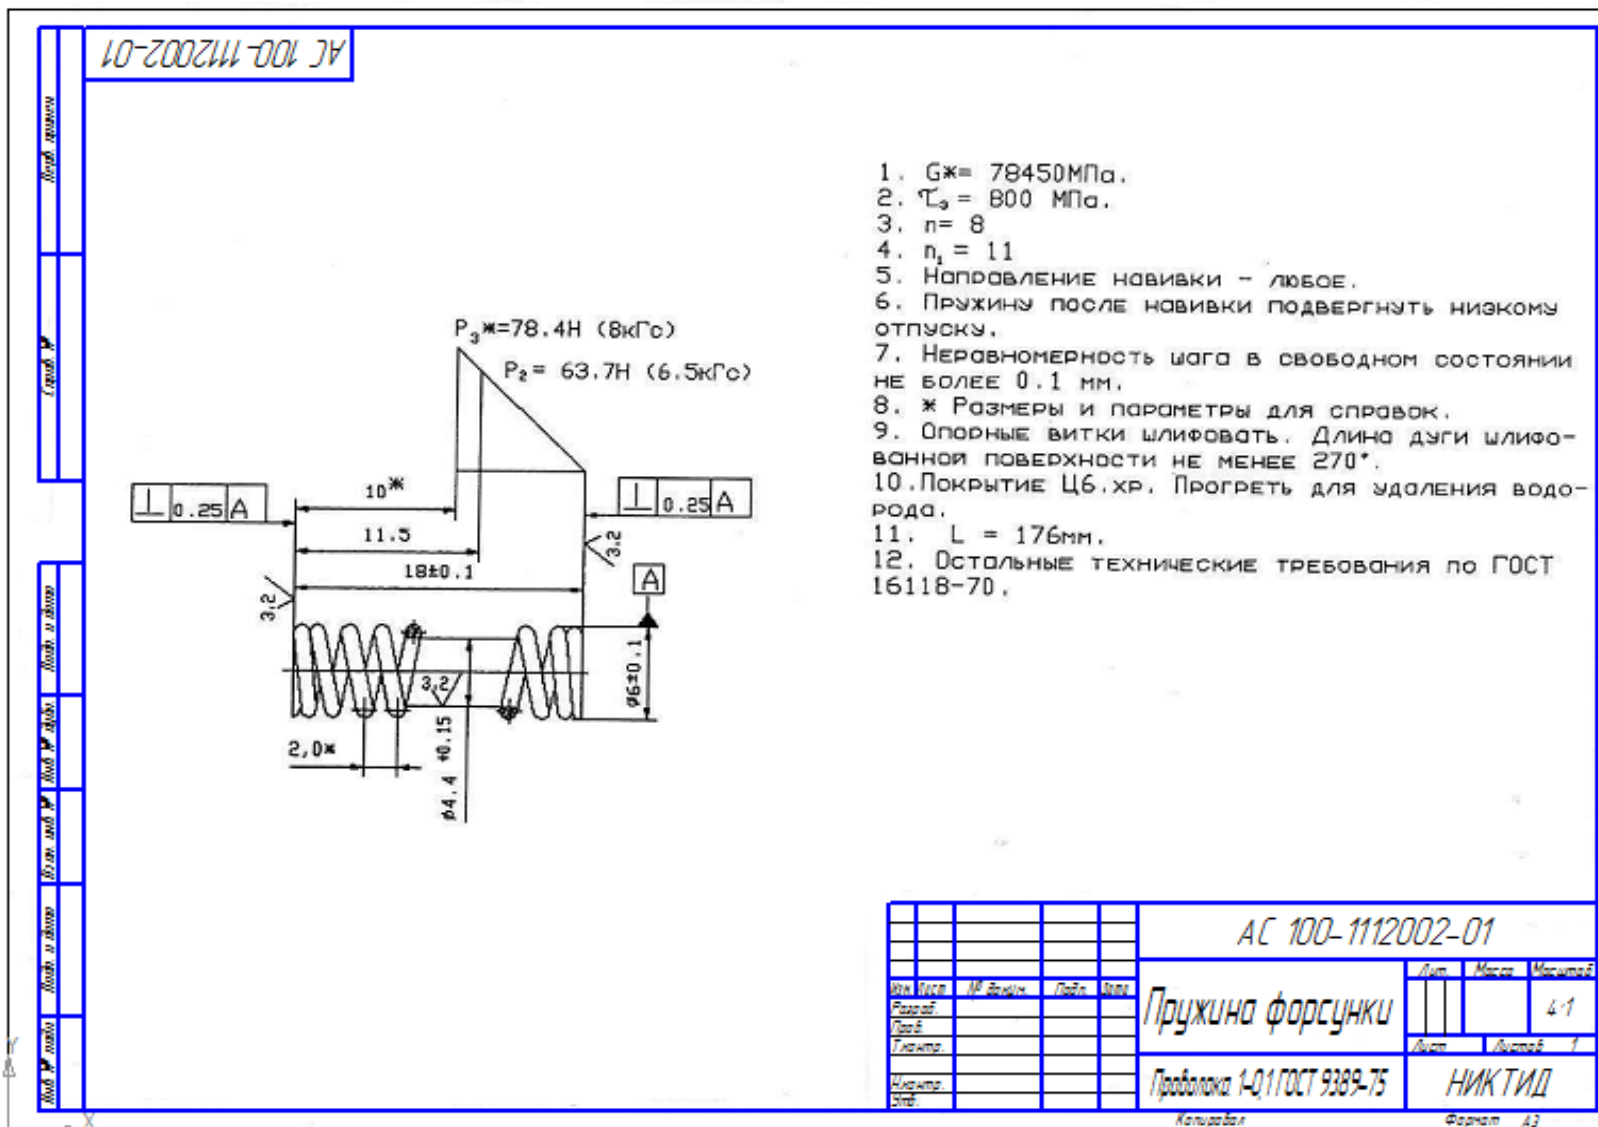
Пример выполнения рабочего чертежа детали «Пружина форсунки»
